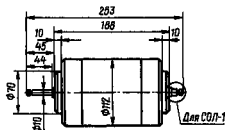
Габаритные и установочные размеры двигателей СОЛ-1
